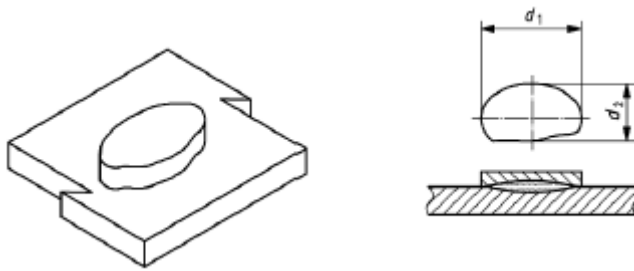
Ponto de Soldadura após Tear Down, Pull out Failure
